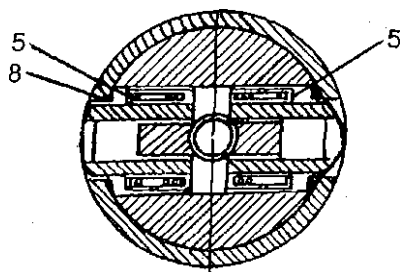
Схема устройства двухрезцового вибрационного пробоотборника конструкции И.Б.Булнаева:
